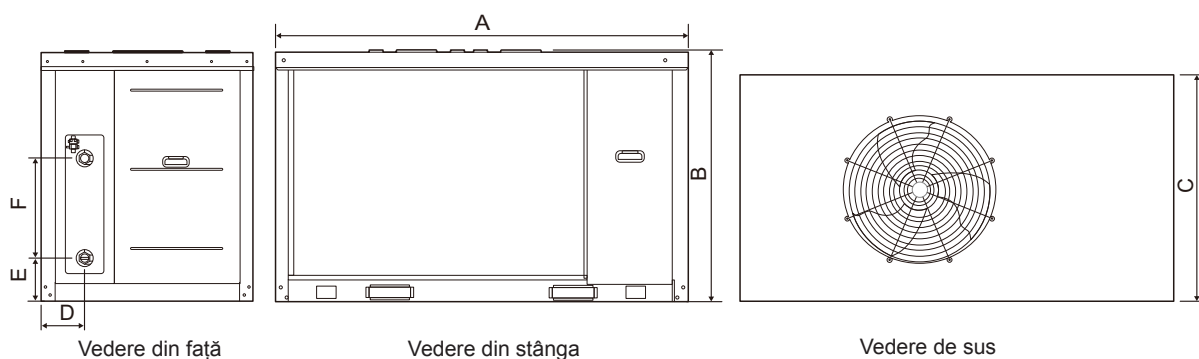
Schema dimensională a KEM-30 DRS4.1
